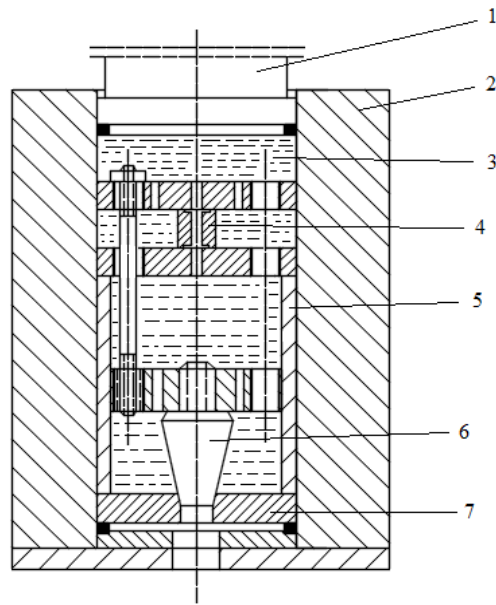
Наладка пластометра для испытания образцов на сжатие (Патент RU 2655043). 1 – пуансон; 2 – герметичный контейнер; 3 – рабочая среда; 4 – испытуемый образец; 5 – стакан; 6 – вспомогательный образец; 7 – матрица
